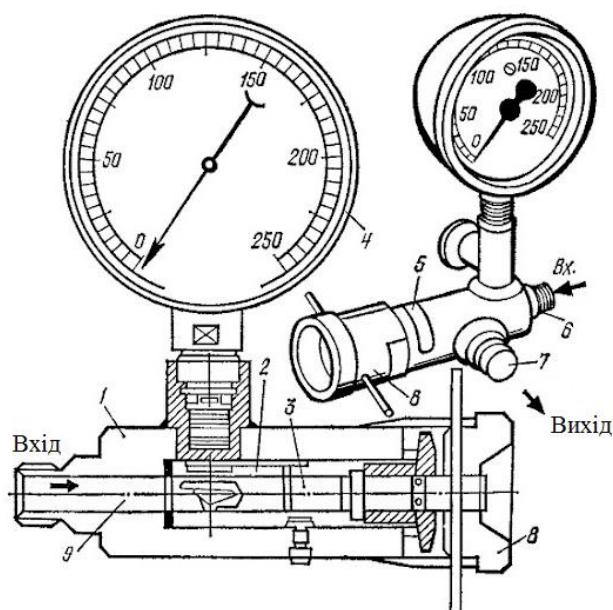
Дросель-витратомір СДР-ЗУК: 1 - корпус; 2 - порожнина; 3 - затвор; 4 - манометр; 5 - шкала; 6 - вхідний штуцер; 7 - вихідний штуцер; 8 - рукоятка; 9 - вхідний канал.
